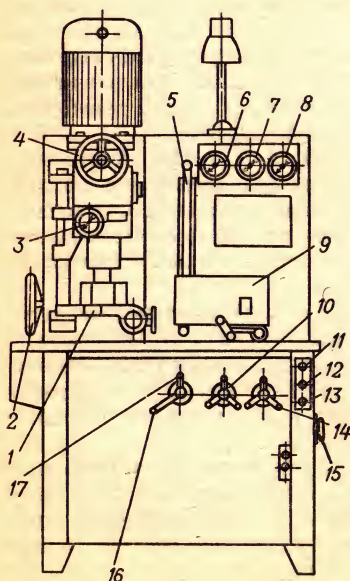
Органы управления и контрольные приборы стенда КИ-5278:
